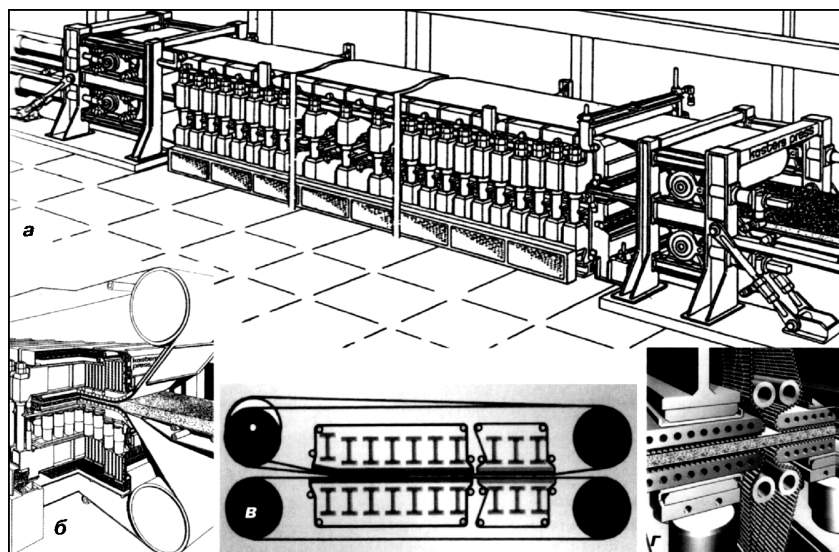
Общая компоновка проходного ленточно-роликового прессы; сверху: принципиальная схема и поперечный разрез зоны прессования:
